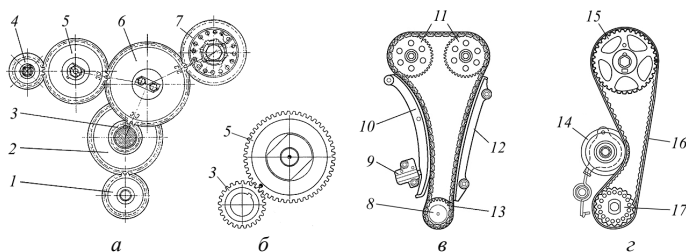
Типы привода распределительного вала: а – зубчатый дизельного двигателя; б – зубчатый бензинового двигателя; в – цепной; г – ременный; 1 – ведомая шестерня привода масляного насоса; 2 – ведущая шестерня привода масляного насоса; 3 – шестерня коленчатого вала; 4 – шестерня привода масляного насоса гидроусилителя руля; 5 – шестерня распределительного вала; 6 – промежуточная шестерня; 7 – шестерня привода топливного насоса; 8 – звездочка коленчатого вала; 9 – натяжитель цепи; 10 – башмак натяжителя; 11 – звездочка распределительного вала; 12 – успокоитель; 13 – цепь; 14 – натяжной ролик; 15 – шкив распределительного вала; 16 – зубчатый ремень; 17 – шкив коленчатого вала
